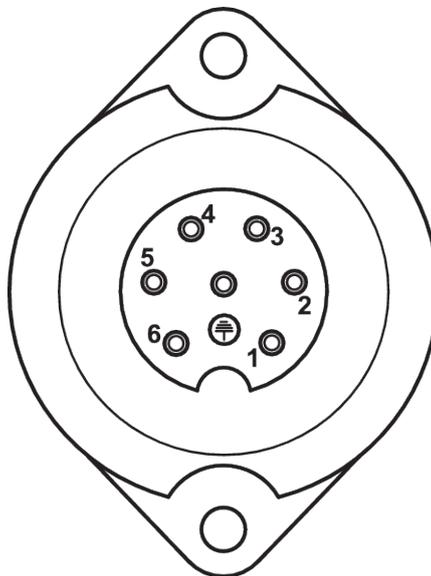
PIN-Belegung der 7-poligen Steckverbindung
